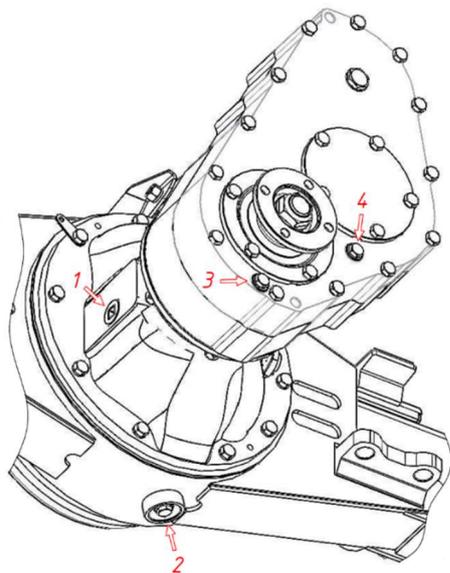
Расположение пробок картеров главной передачи и проходного редуктора
